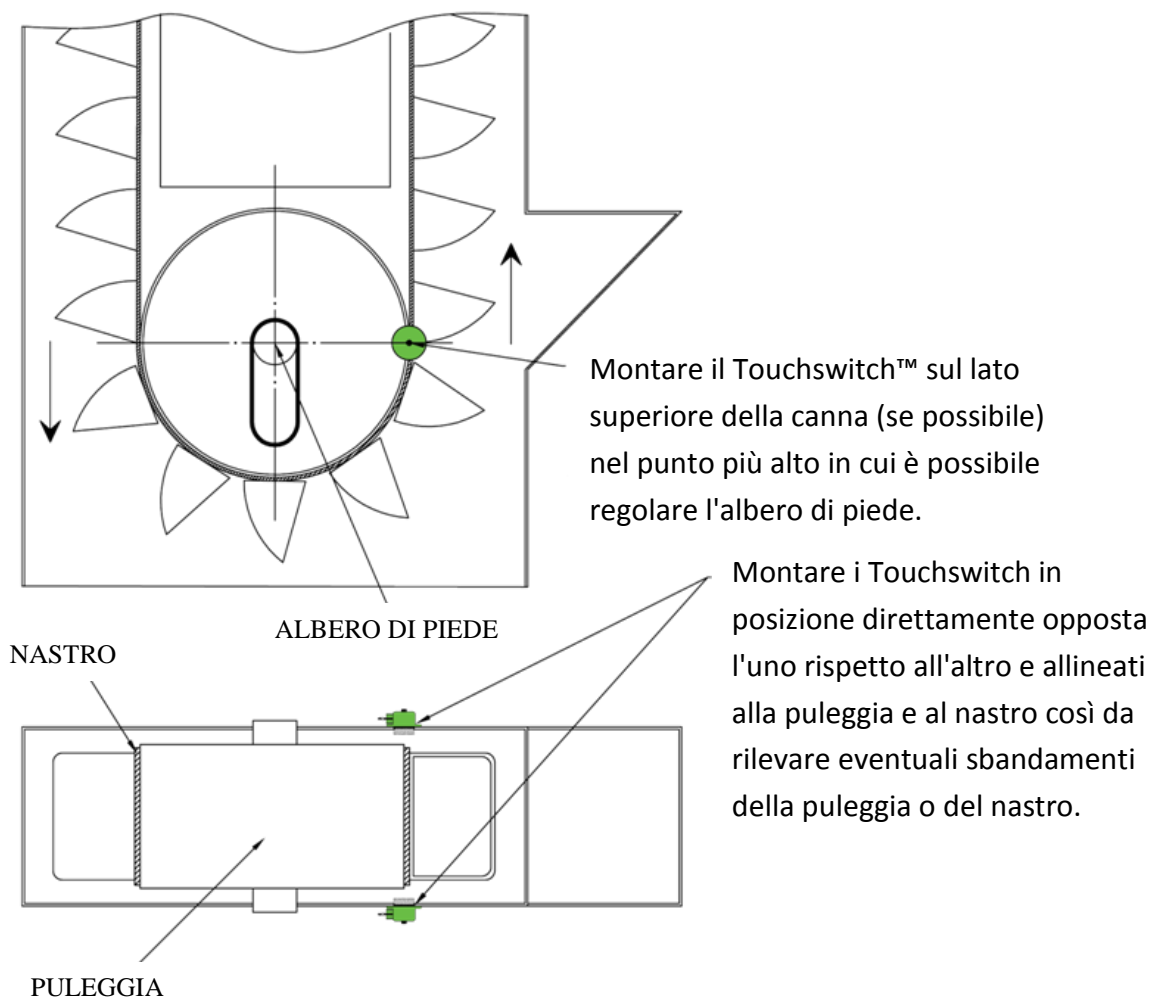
Posizione di montaggio del Touchswitch – Puleggia inferiore
